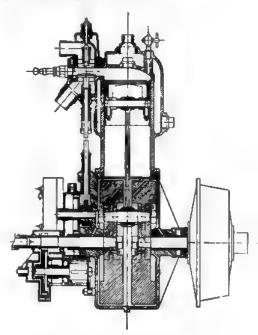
Schnitt durch 1 cyl. Motor u. Pumpe.
